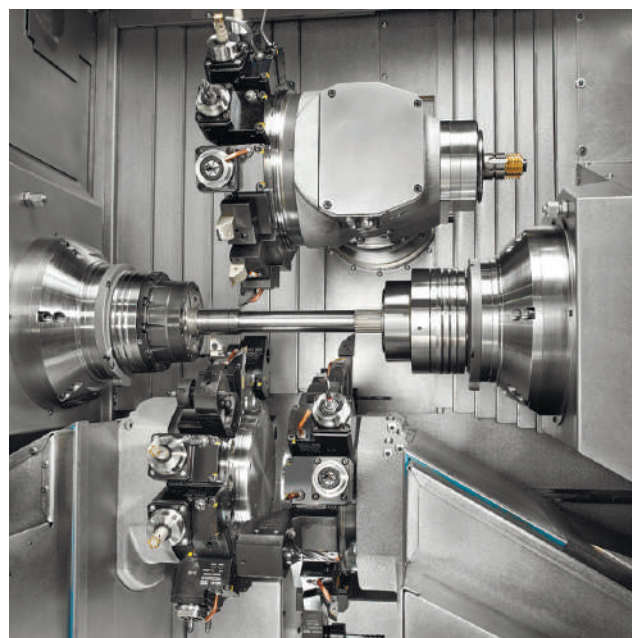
Комбинация с двумя револьверными головками и верхним суппортом с осью В, фрезерным шпинделем и револьверной головкой — 4 инструментальных суппорта
